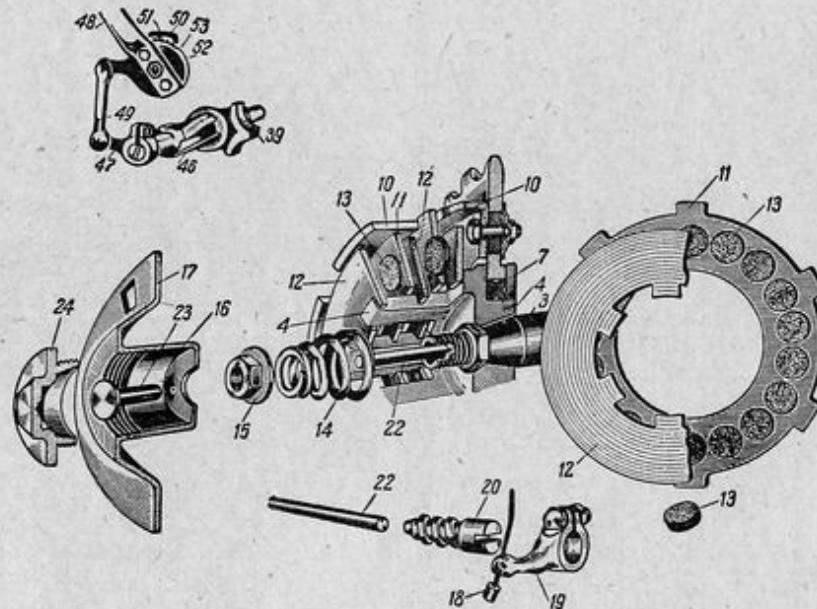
Детали муфты сцепления (Л-300, ИЖ-8):
